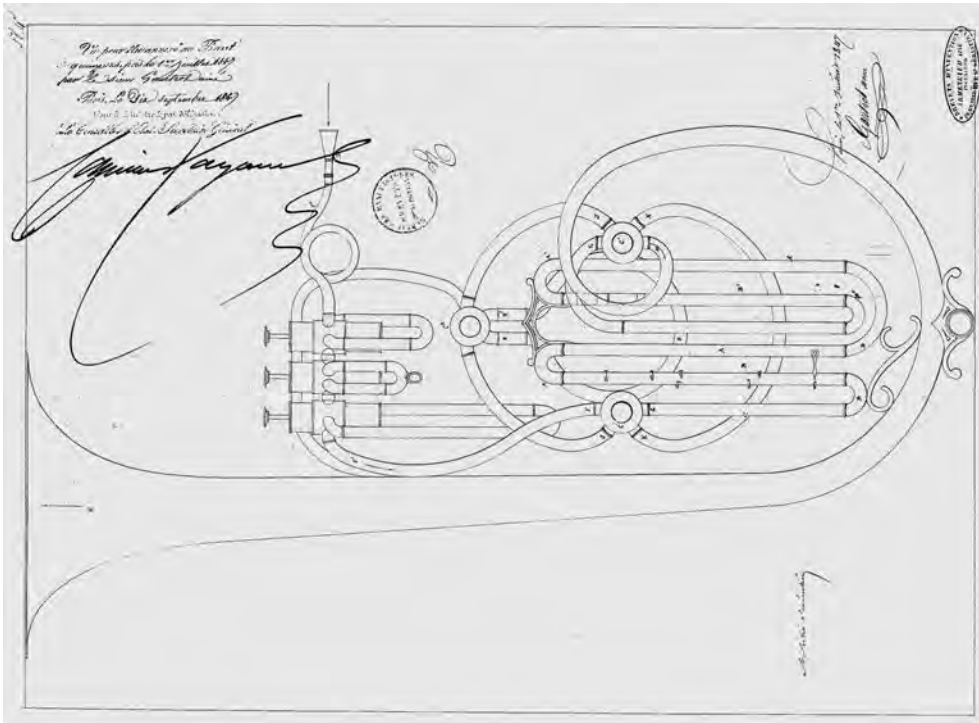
Dessin du brevet 5874 du 1^{er} juillet 1847, planche 4
